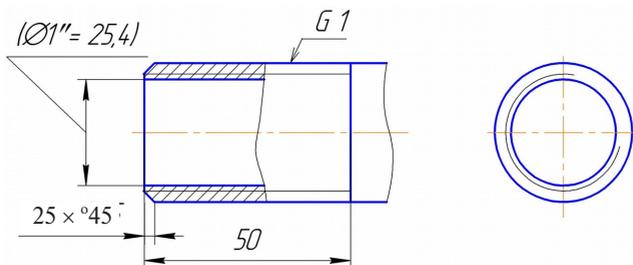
Изображение и обозначение резьбы трубной цилиндрической
